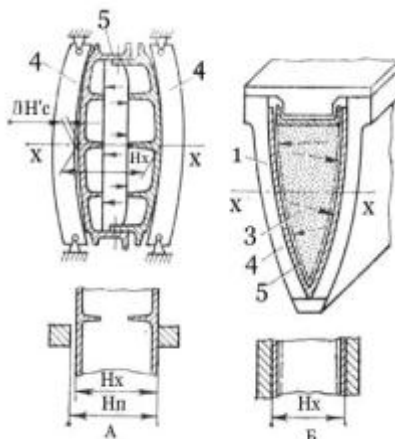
Схемы базирования по наружной поверхности обшивки:
